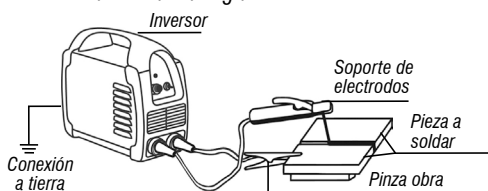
Montaje de cables de soldadura para la soldadura con electrodo revestido (MMA)
